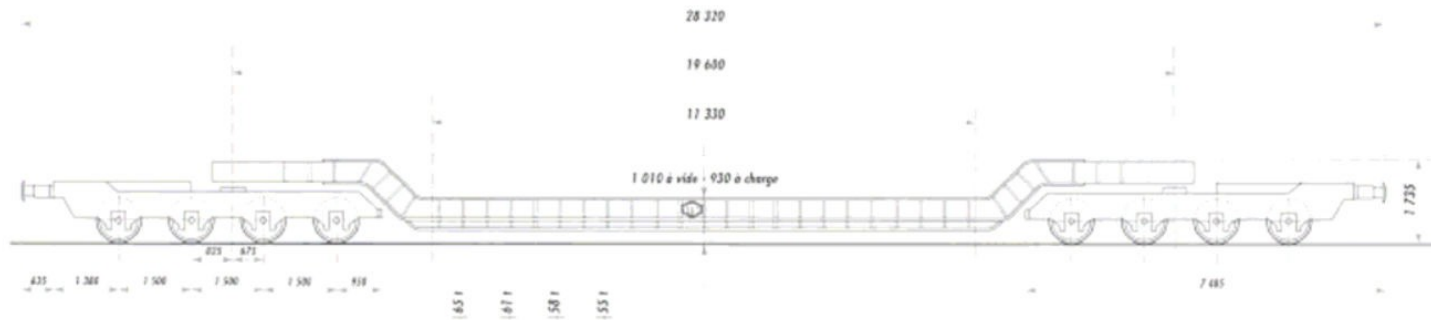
Wagon à plancher surbaissé (Crédits : Maxifret (SNCF))
